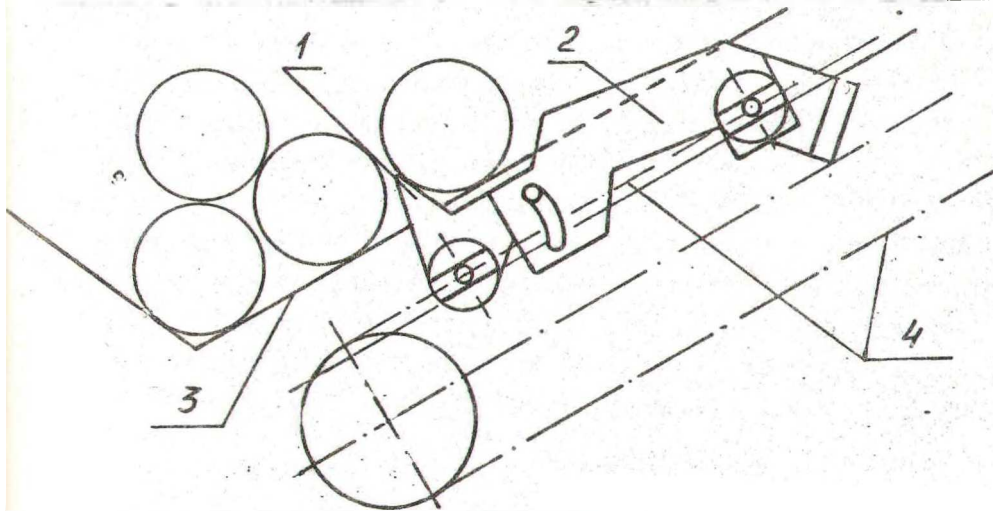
Принципиальная схема захватного механизма со сложной формой прорези: 1 - кривошип; 2 - кулиса; 3 - направляющие слезги; 4 - тяговая цепь
